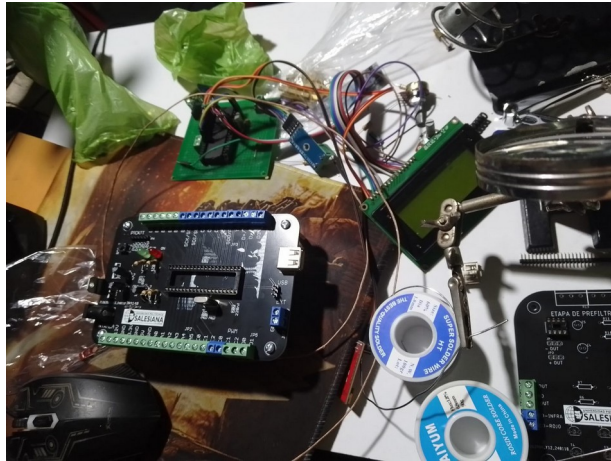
Proceso de Soldadura para la Tarjeta Interfaz con el PIC
